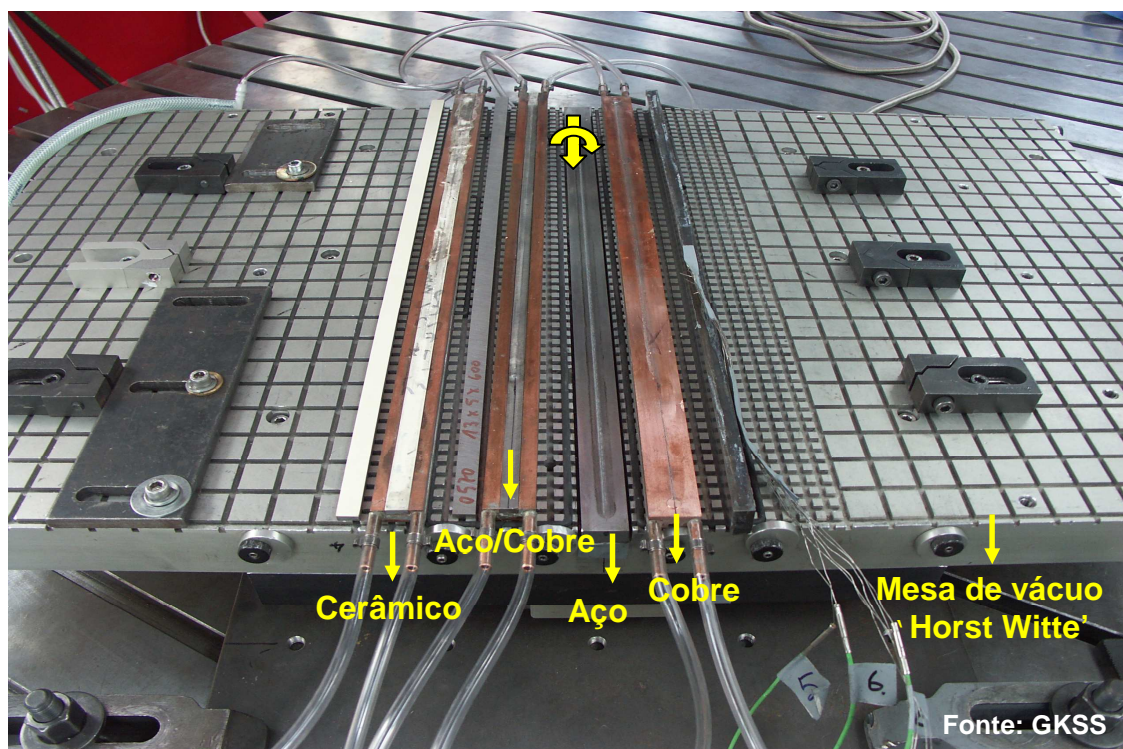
Backing* de diferentes materiais utilizados no processo FSW sob a mesa com sistema de fixação mecânica e a vácuo das chapas soldadas.
